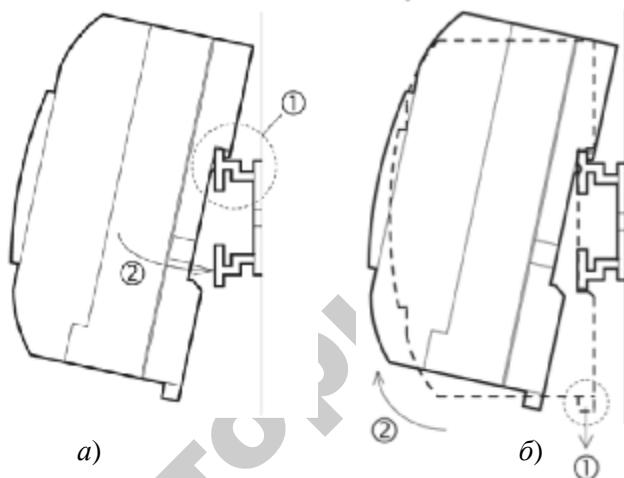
Установка (а) и отсоединение (б) контроллера (2) при использовании DIN-рейки (1)
